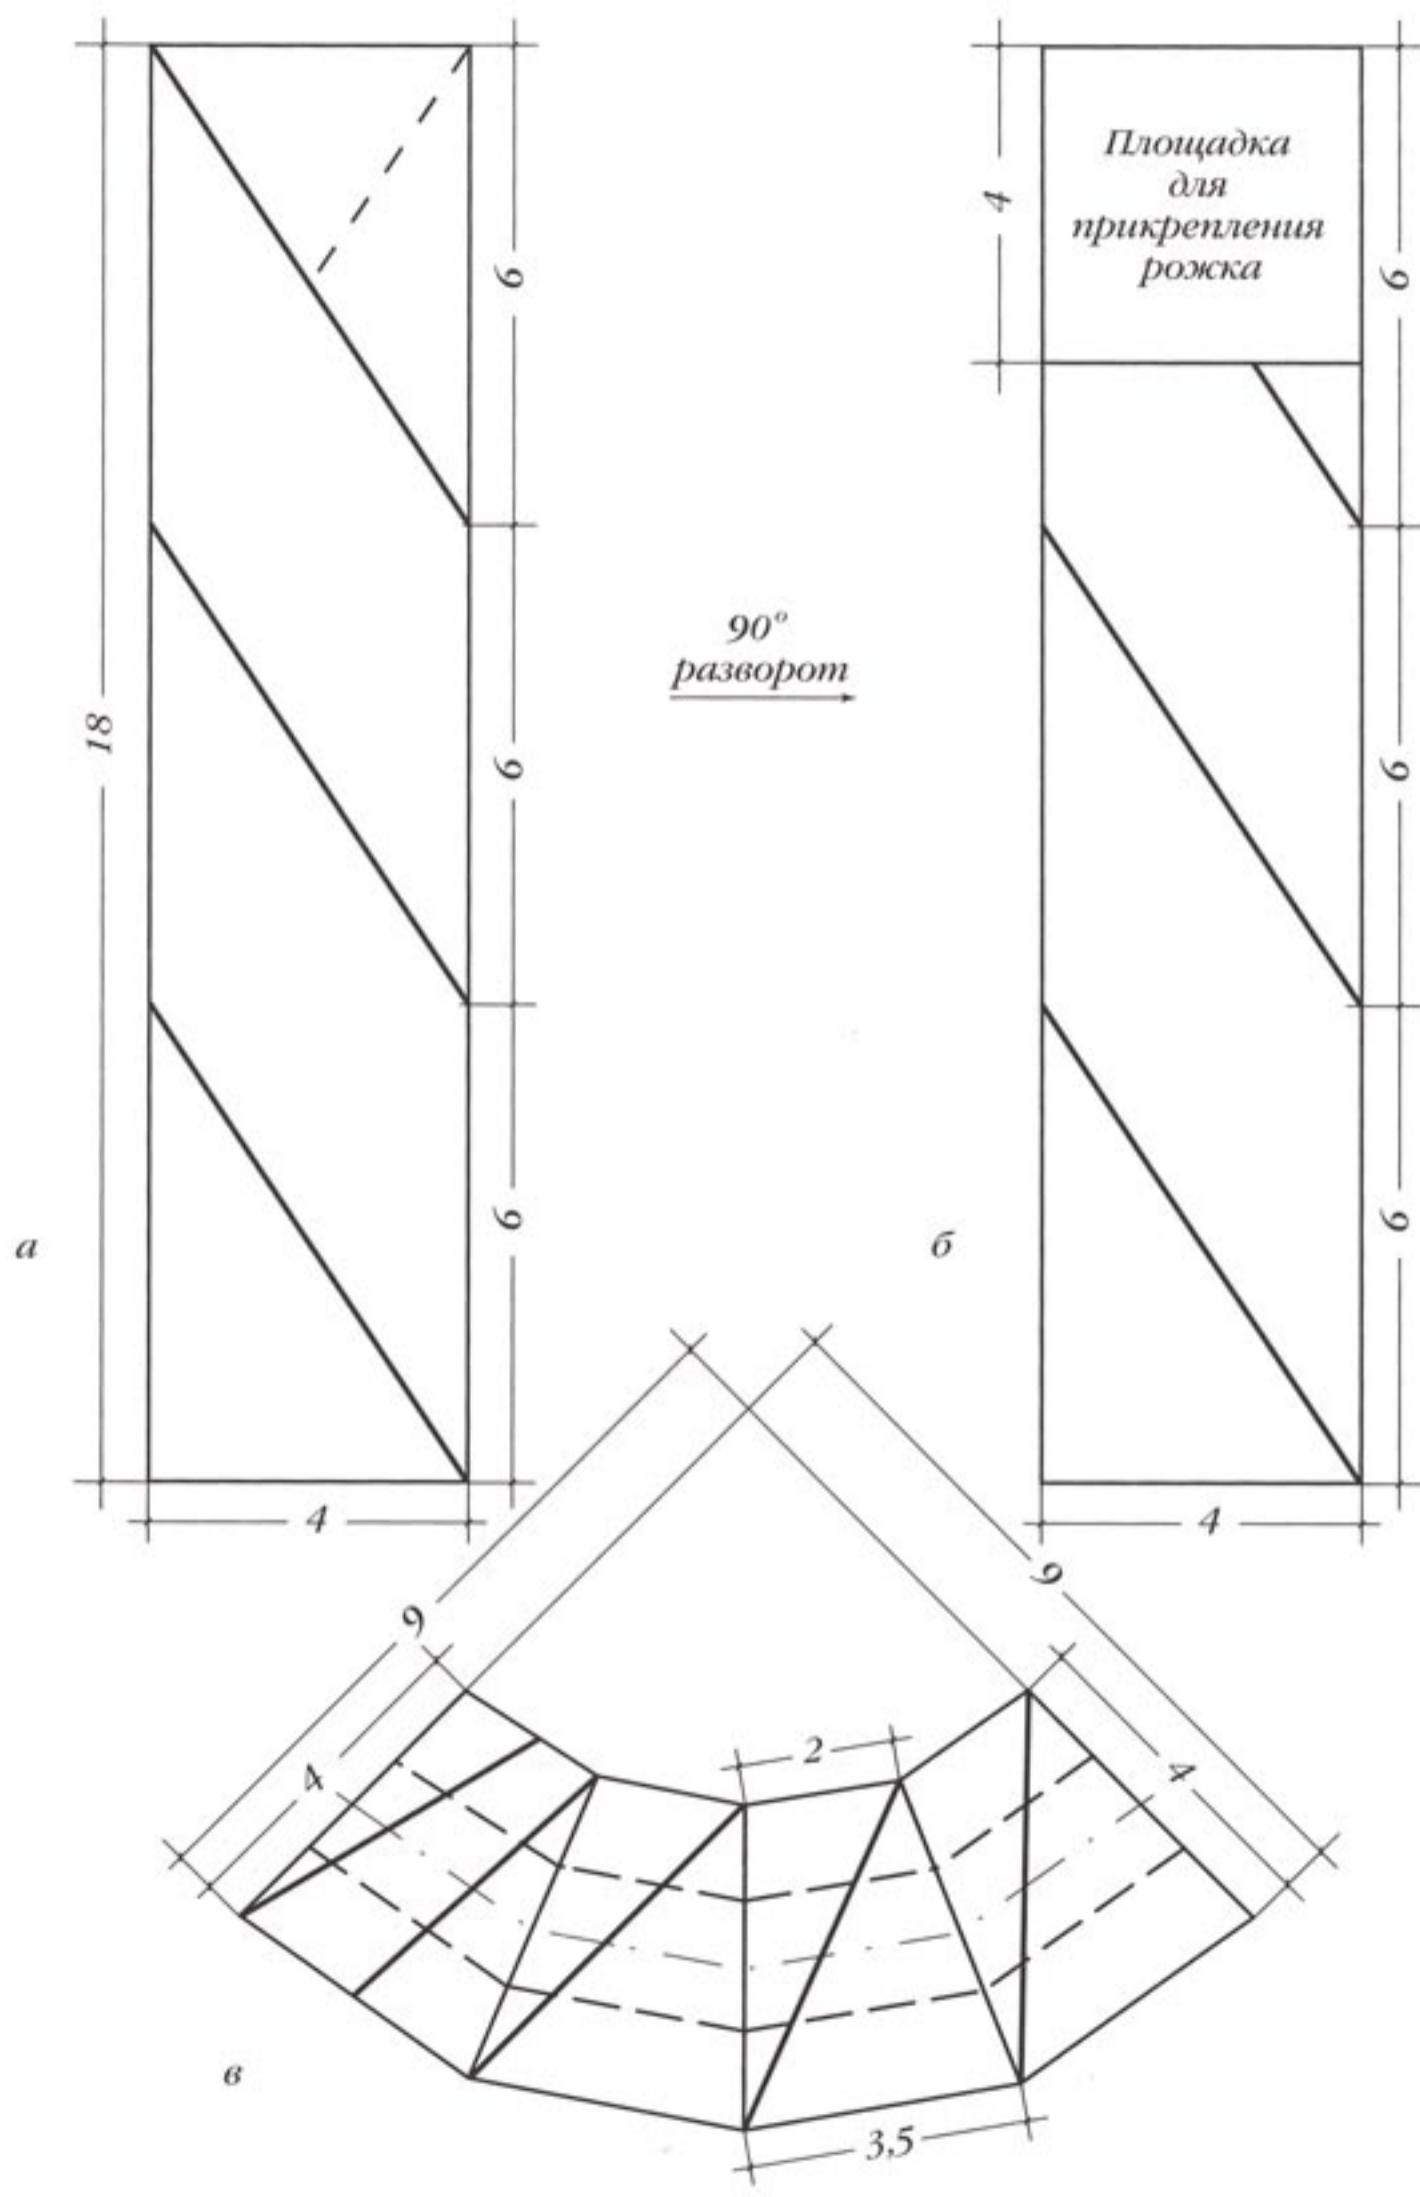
Схема разметки стойки (а, б; двухзаходный винт; шаг 6) и рожка (в; четырехзаходный винт) двухсвечника к рис. 178
